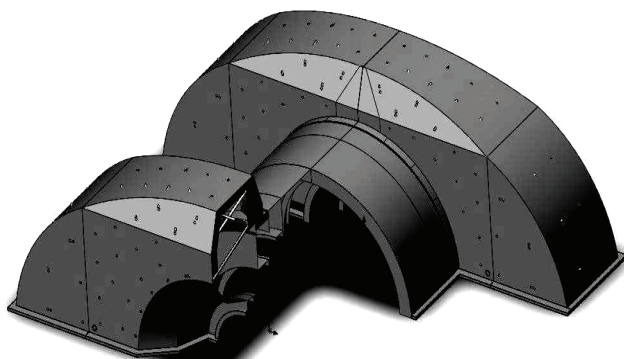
Геометрическая модель верхней части корпуса паровой турбины
